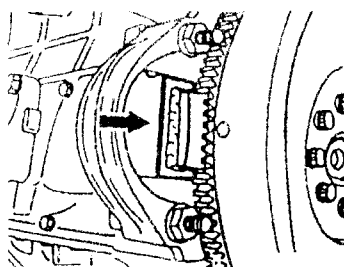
Ttraba del giro de motor 602 589 00 40 00
